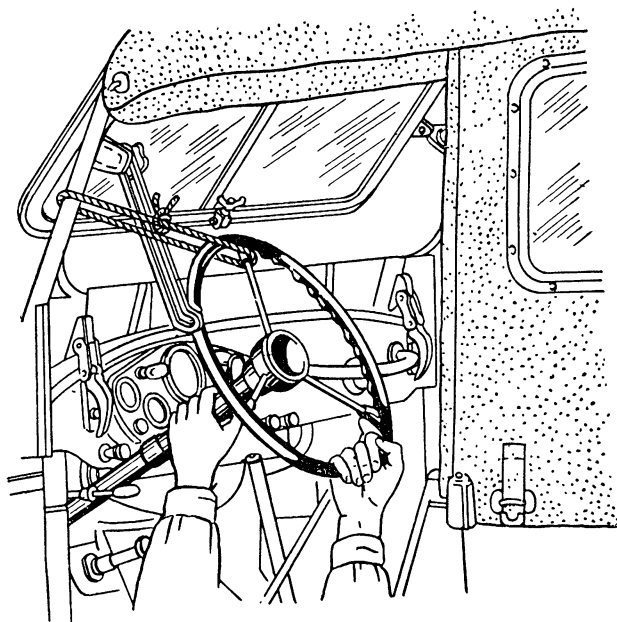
Проверка осевого люфта в подшипниках червяка рулевого механизма
